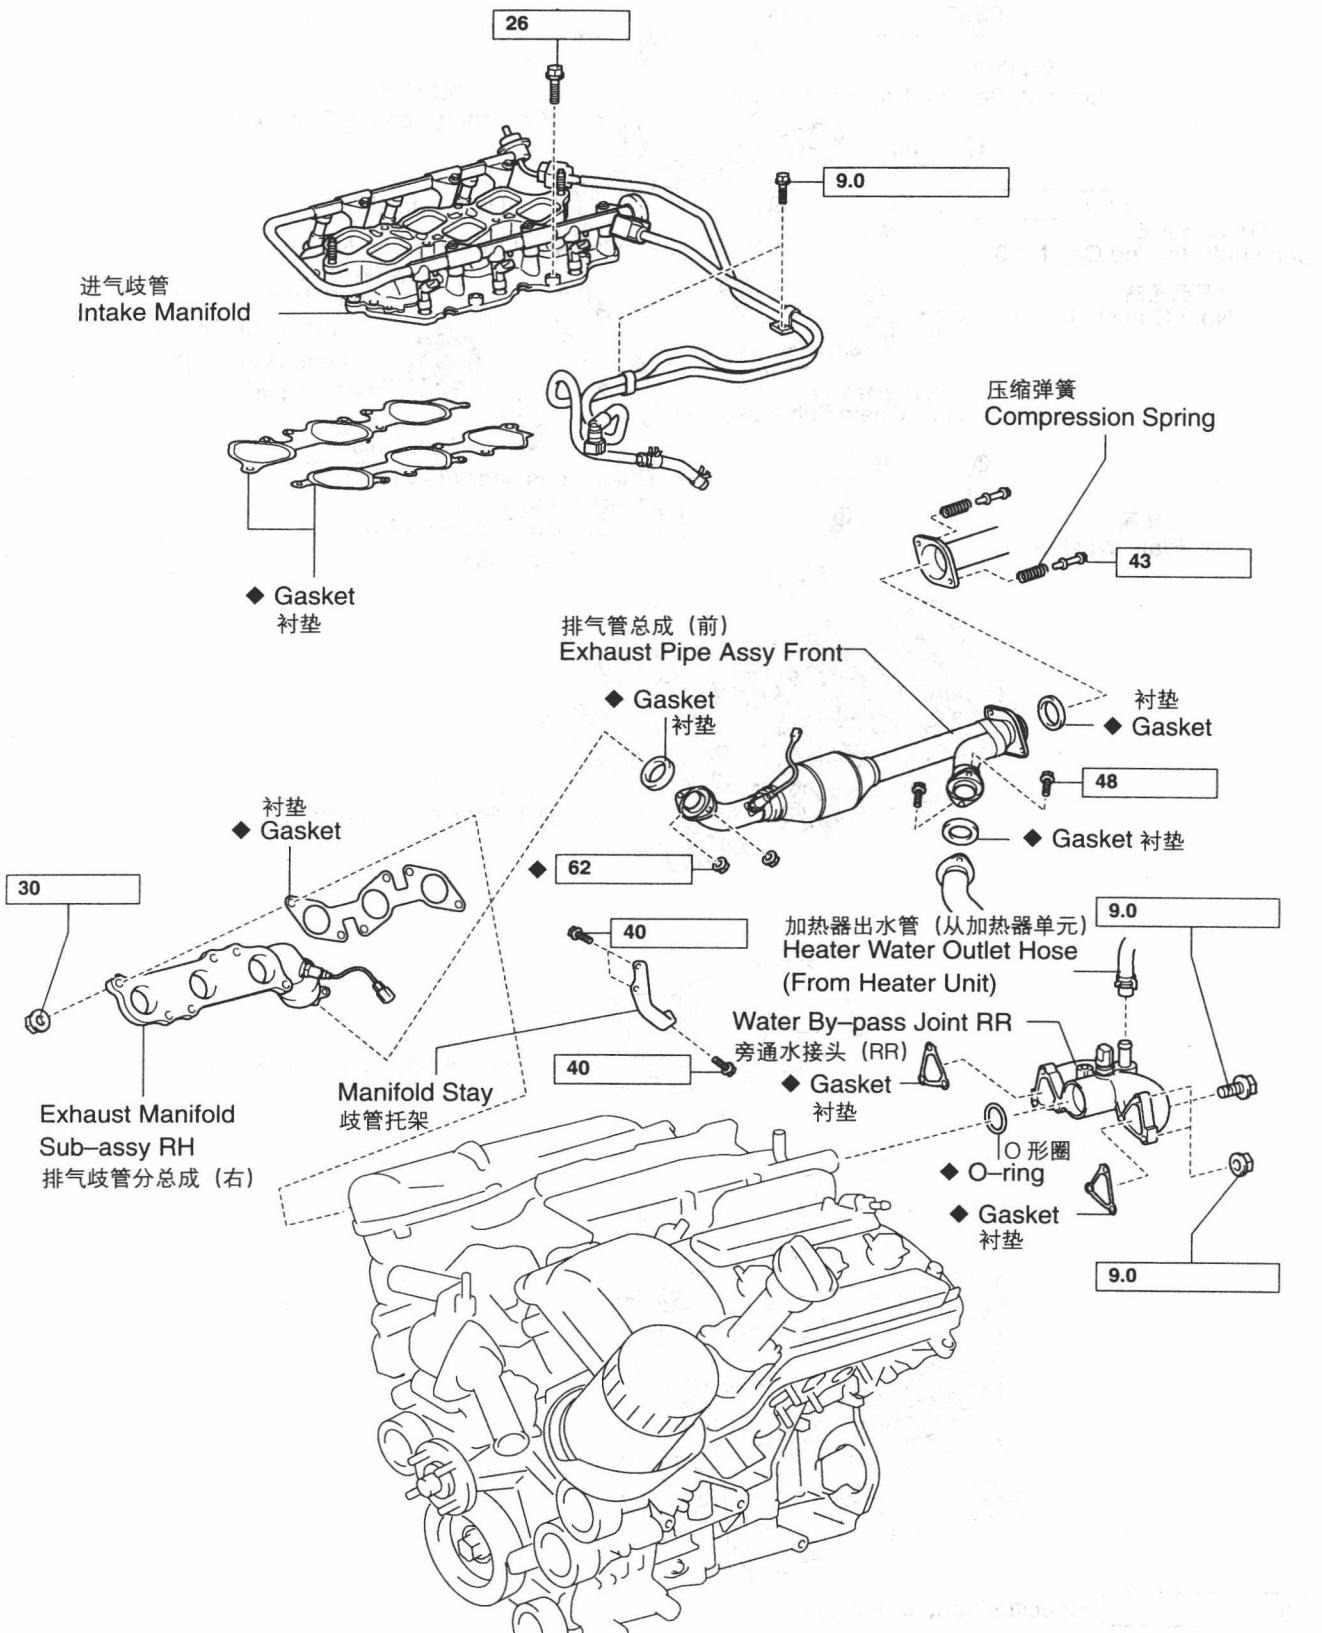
发动机总成 (ENGINE ASSEMBLY) (5)
